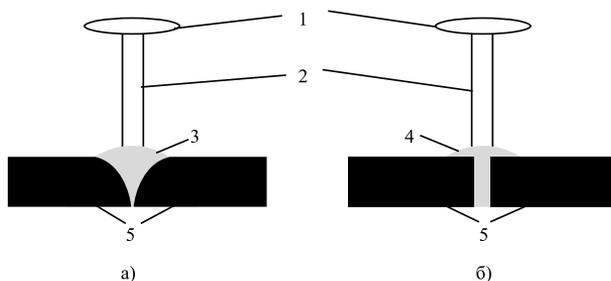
Схема лазерной сварки а) и пайки б)
